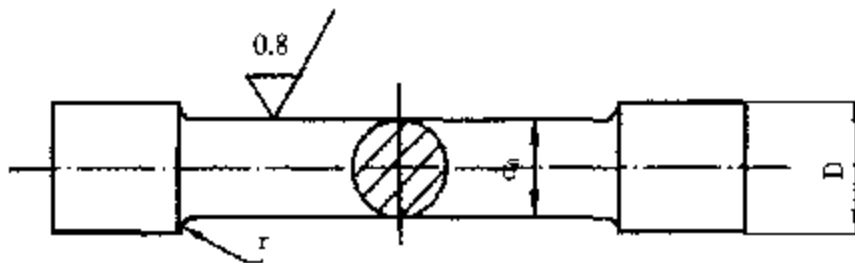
焊接材料熔敷金属拉伸试样示意图
